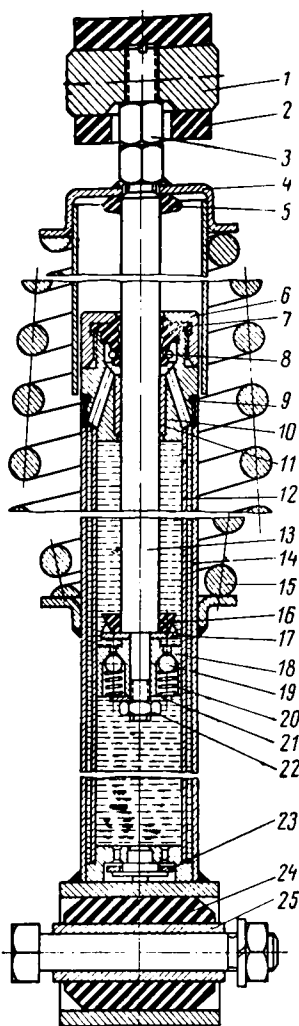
Задний амортизатор мото-роллера ВП-150:
